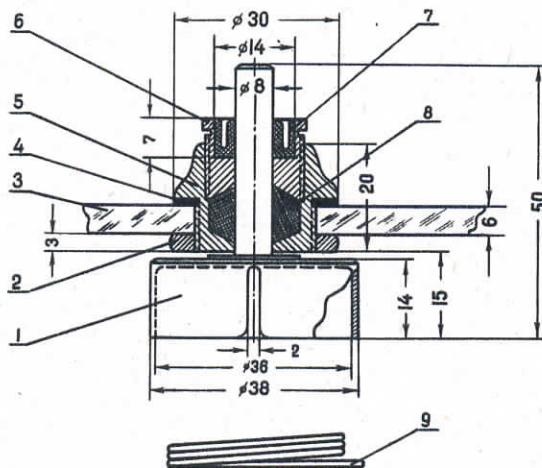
Механизм перемотки пленки: 1 — барабан; 2 — гайка; 3 — крышка бокса; 4 — резиновая прокладка; 5 — корпус сальника; 6 — уплотнительная гайка; 7 — самоуплотняющаяся манжета; 8 — сальник; 9 — пружина
